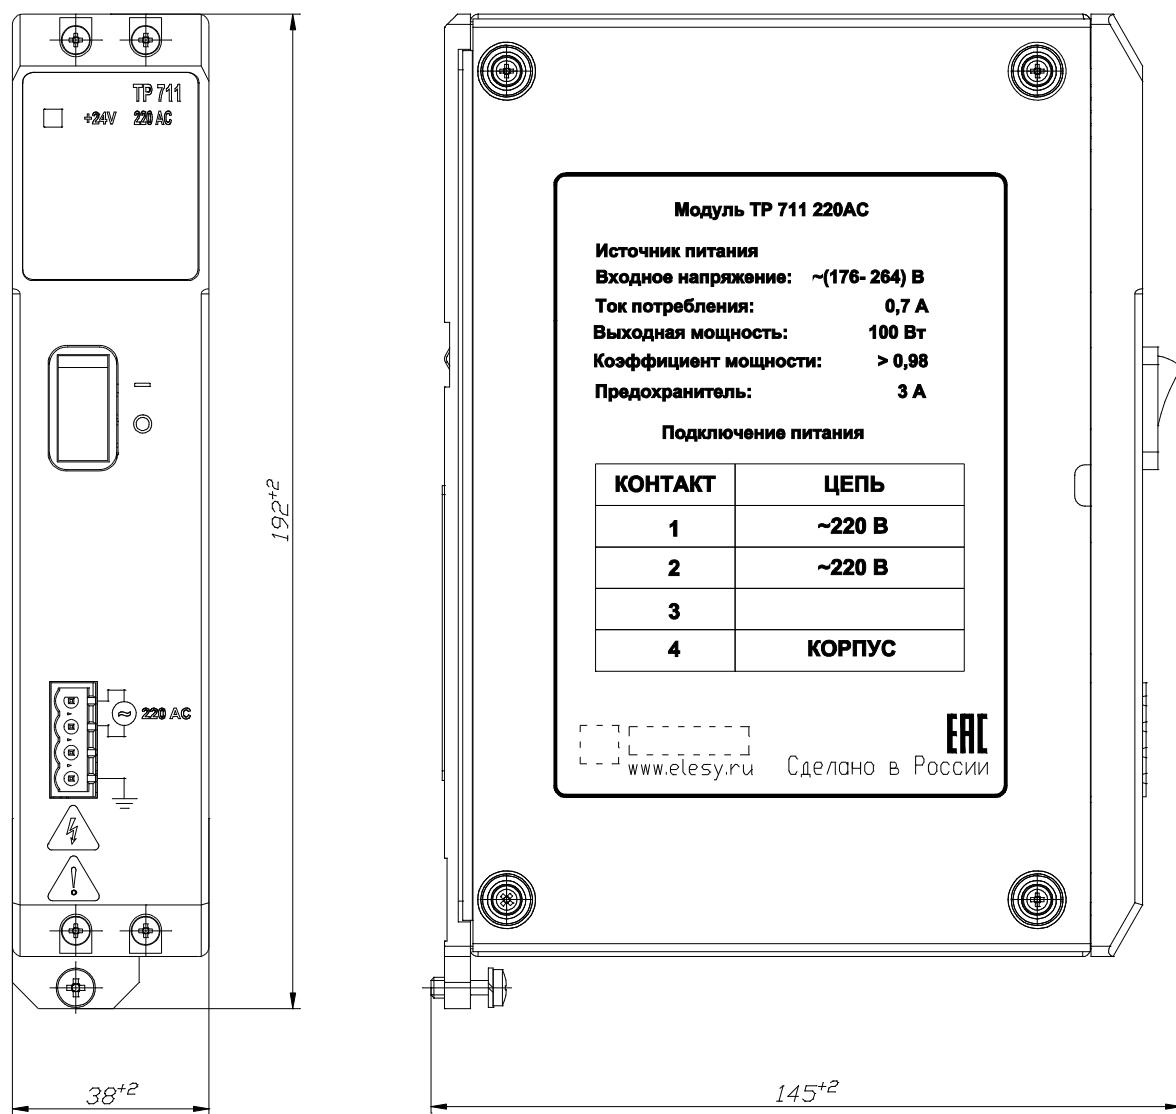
Внешний вид и габаритные размеры модуля
